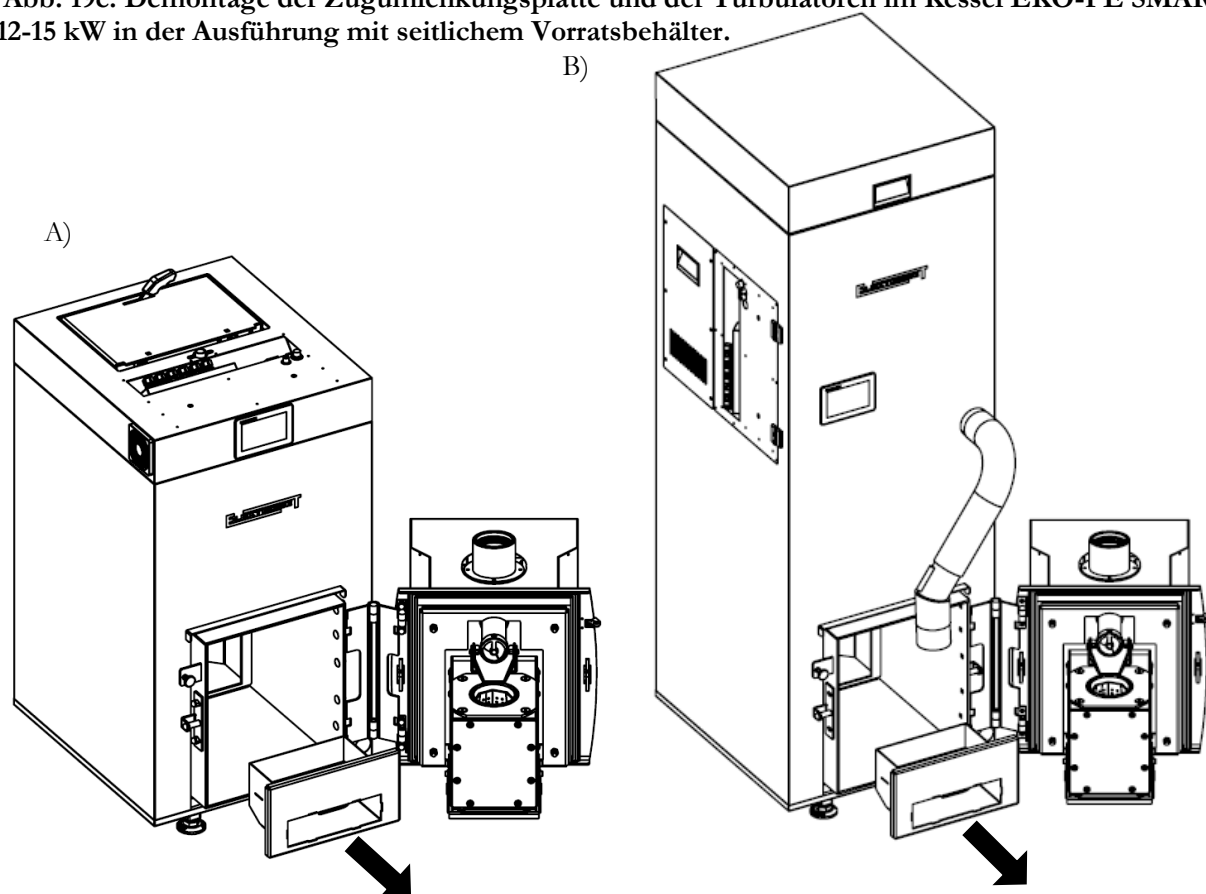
Reinigen der hinteren Aschelade im Kessel EKO-PE SMART 12-15 kW in den Ausführungen: (A) - STANDARD und BOX, (B) - TOP
